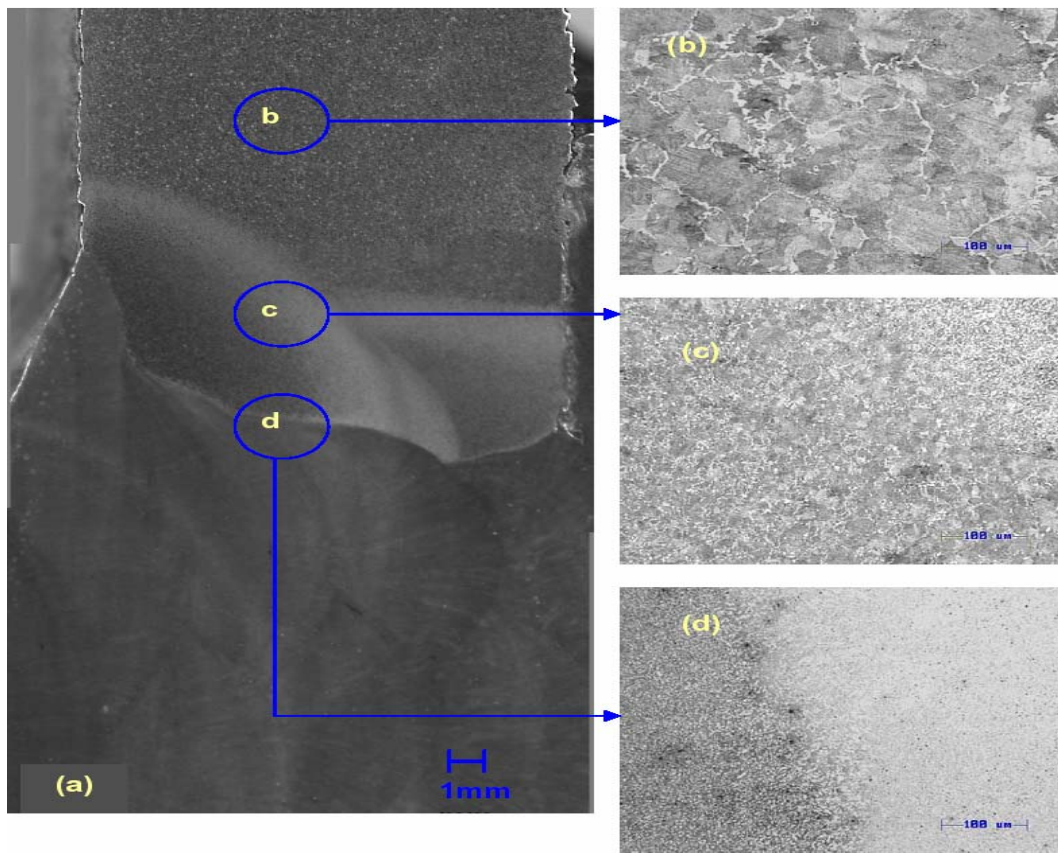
Macrografía del Cordón de Soldadura (a) Vista General; Detalles: (b) Material base, (c) Zona afectada por el Calor, (d) Intercara cordón/ZAC.
